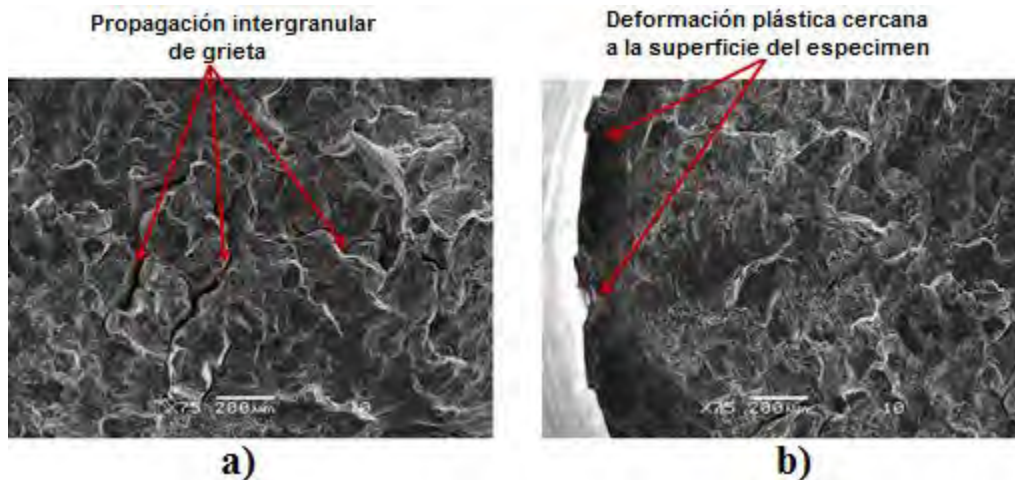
A) Propagación intergranular de grieta al centro del espécimen bajo cargas de torsión, b) alta deformación plástica en la sección angosta del espécimen.
